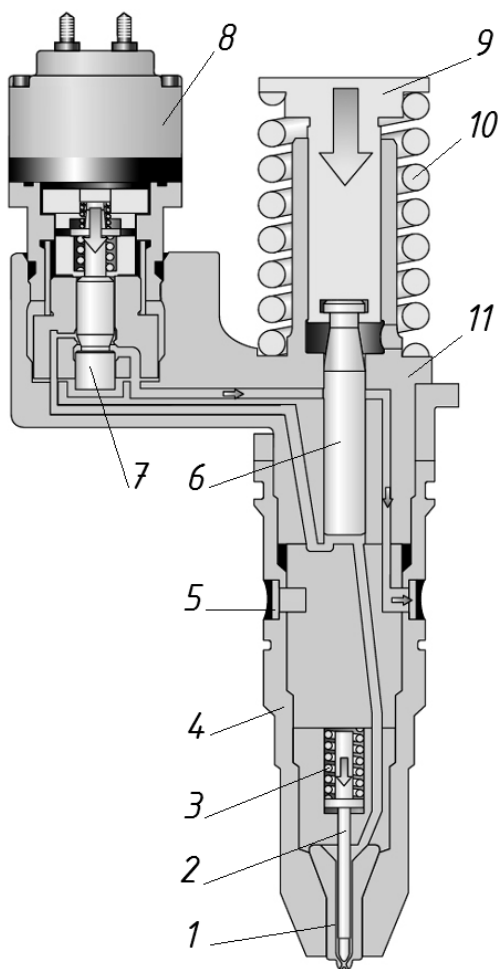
Насос-форсунка з електромагнітним приводом керуючого клапана: 1 – корпус розпилювача; 2 – голчастий клапан; 3 – пружина голчастого клапана; 4 – корпус; 5 – магістраль низького тиску; 6 – плунжер; 7 – клапан; 8 – соленоїд; 9 – штовхач; 10 – пружина штовхача; 11 – втулка
